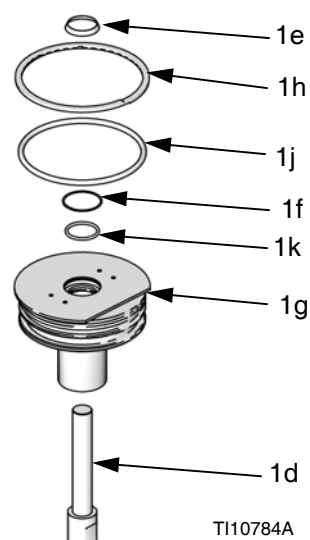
Joint de tige de piston de 165,1 mm (6,5 po.)
